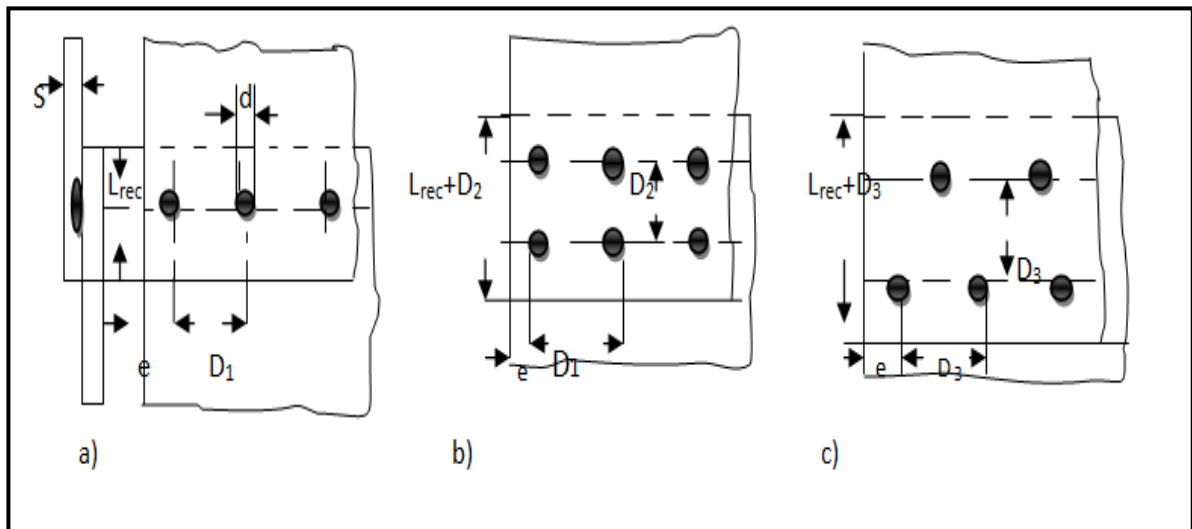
Dispositions des soudures par points : a) joint en rangée, b) joint en chaines, c) joint en quinconces [19].
